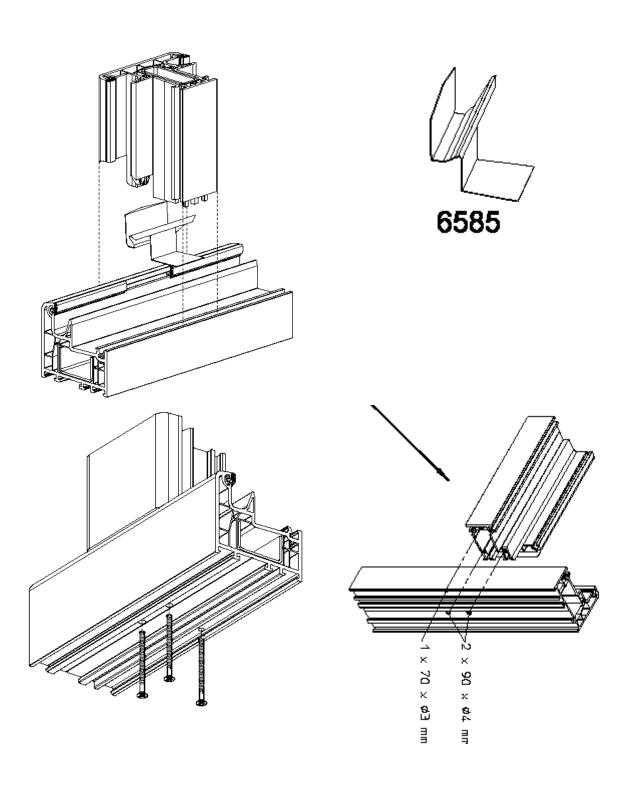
Assemblage mécanique en T de type assemblage par vis
